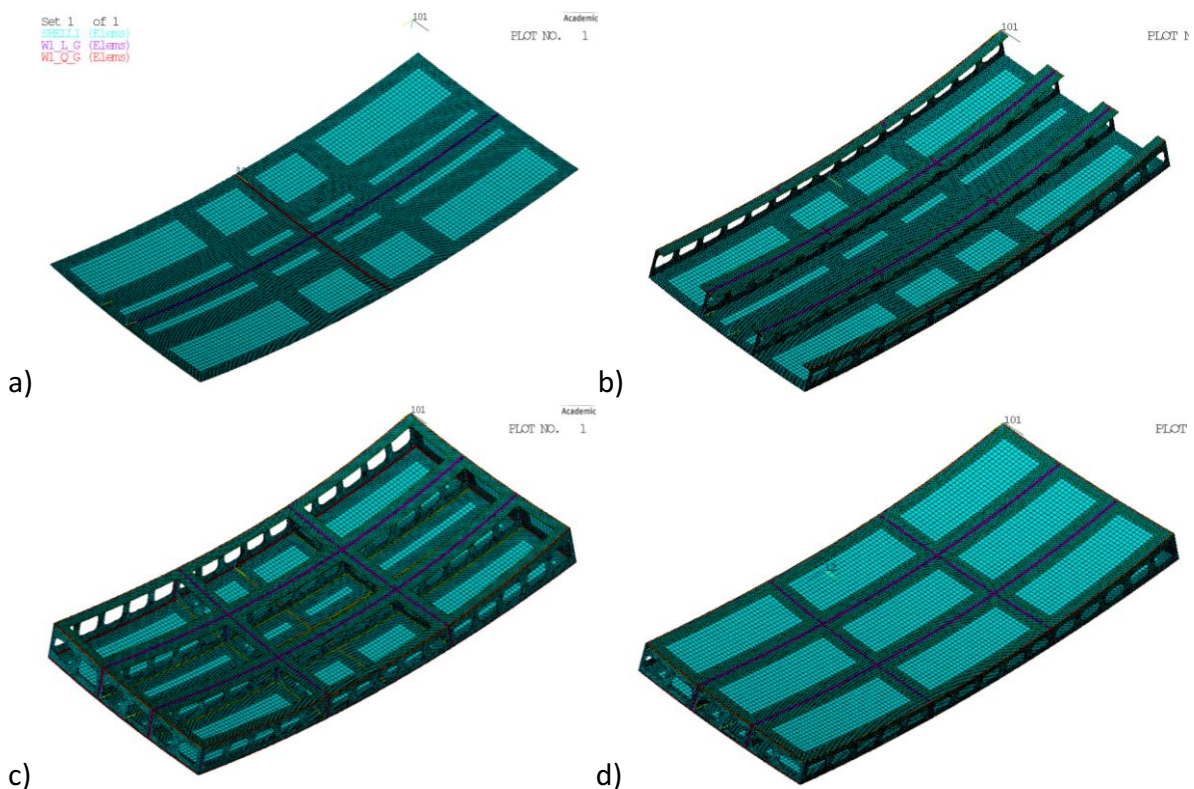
Fertigungsschritte: a) Schweißen der Oberschale, (b) Schweißen der Längsbalken, (c) Schweißen der Querbalken und (d) Schweißen der Unterschale
